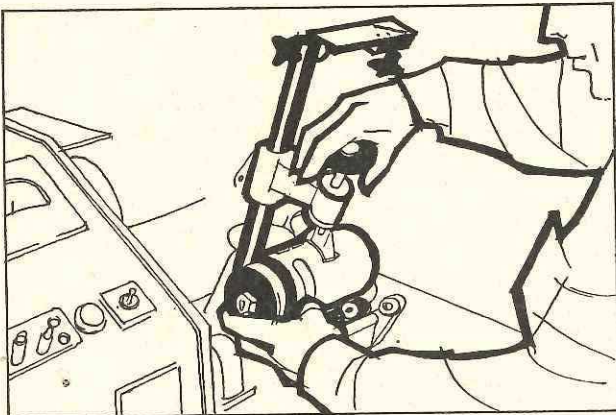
Das Aufspannen eines Kollektor-Generators auf den Siegel-Lichtmaschinenprüfstand.
